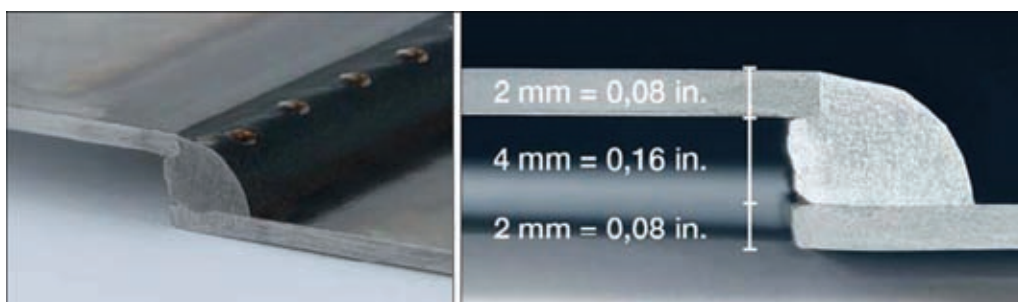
Сварка обычной конструкционной стали методом CMT Advance
